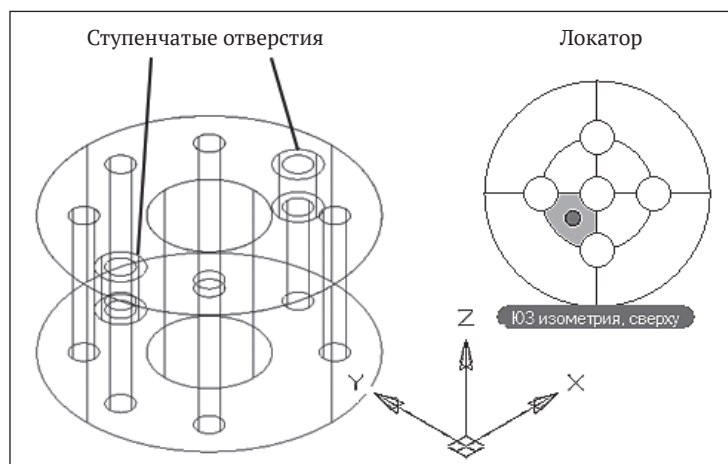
Построение двух ступенчатых отверстий в промежуточном виде 3D-модели детали «Корпус»
